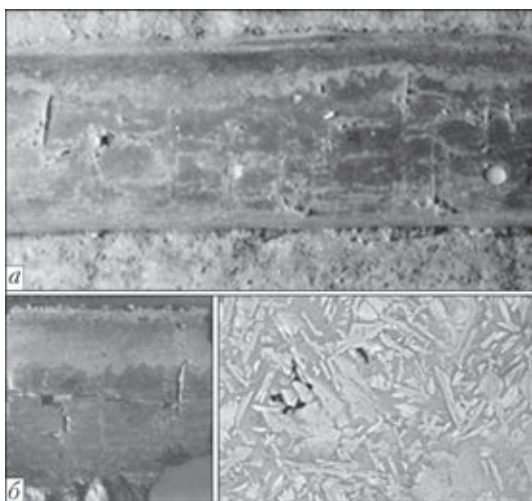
Поверхность металла шва и шлаковой корки при наплавке под флюсом ДФК-2: а — макрошпинели на поверхности металла шва ($\times 2$); б — макро- и микроизображение шлаковой корки ($\times 1500$)
